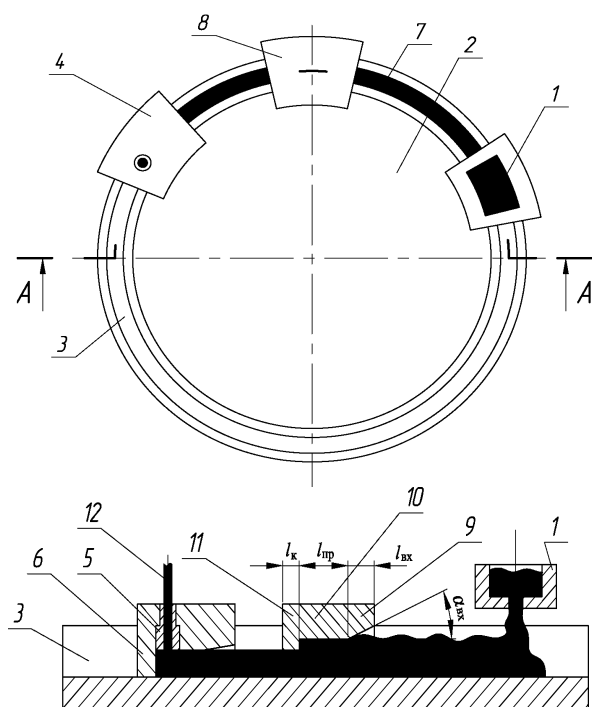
Схема установки непрерывного литья и прессования методом Конформ: 1 - печь-миксер с дозатором 2 - кристаллизатор; 3 - кольцевая канавка 3; 4 - основной неподвижный дугообразный сегмент; 5 - матрица; 6 - выступ; 7 - зона кристаллизации металла; 8 - промежуточная неподвижная сегментная вставка; 9, 10 - участки промежуточной неподвижной сегментной вставки; 11 - выступ
